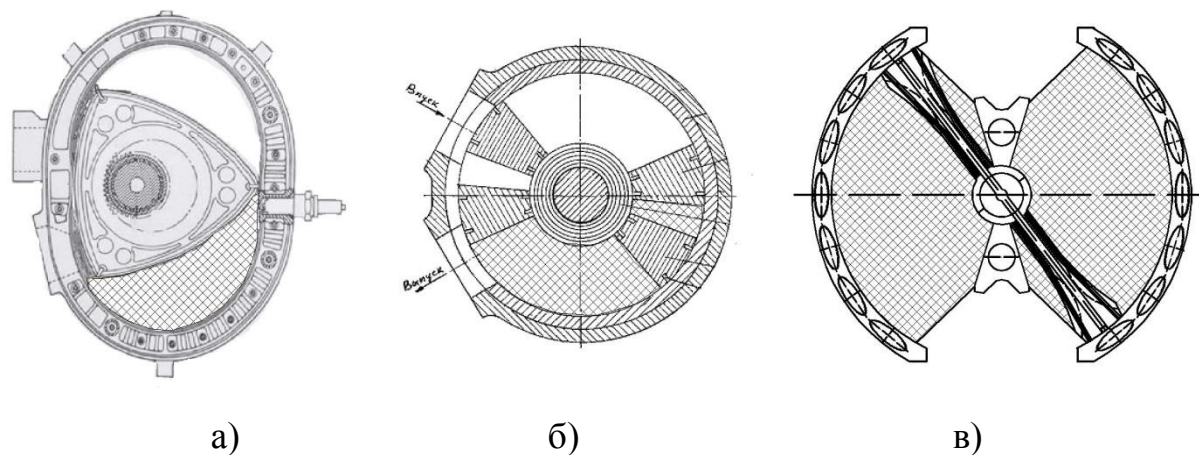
Рабочие объемы двигателей разных конструкций:
